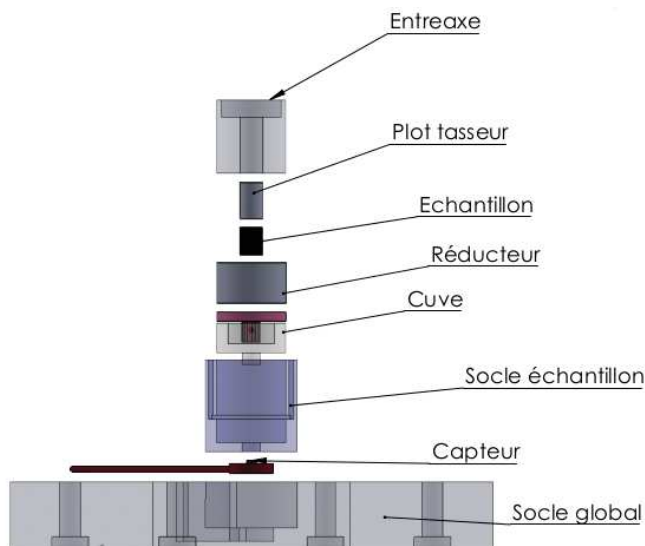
Schéma définitif avant usinage (il manque le joint sur ce schéma) – Vue éclatée de la machine à compaction (Schéma C. Spingarn)
